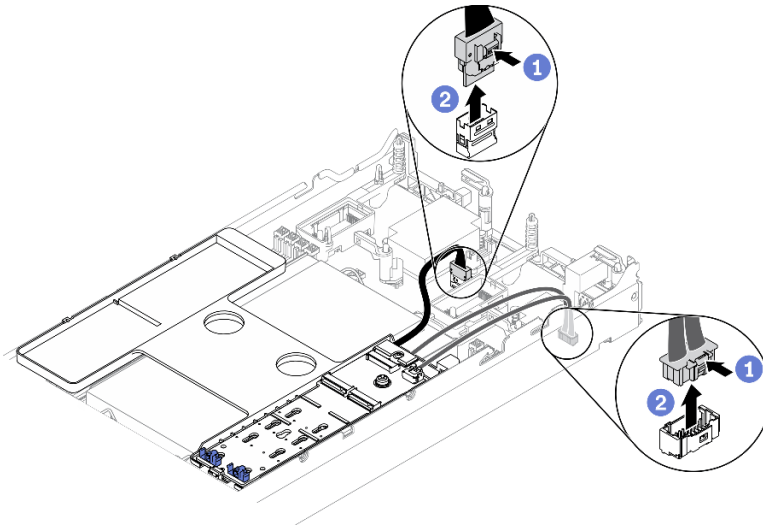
Débranchement des câbles du fond de panier M.2 de la carte mère
